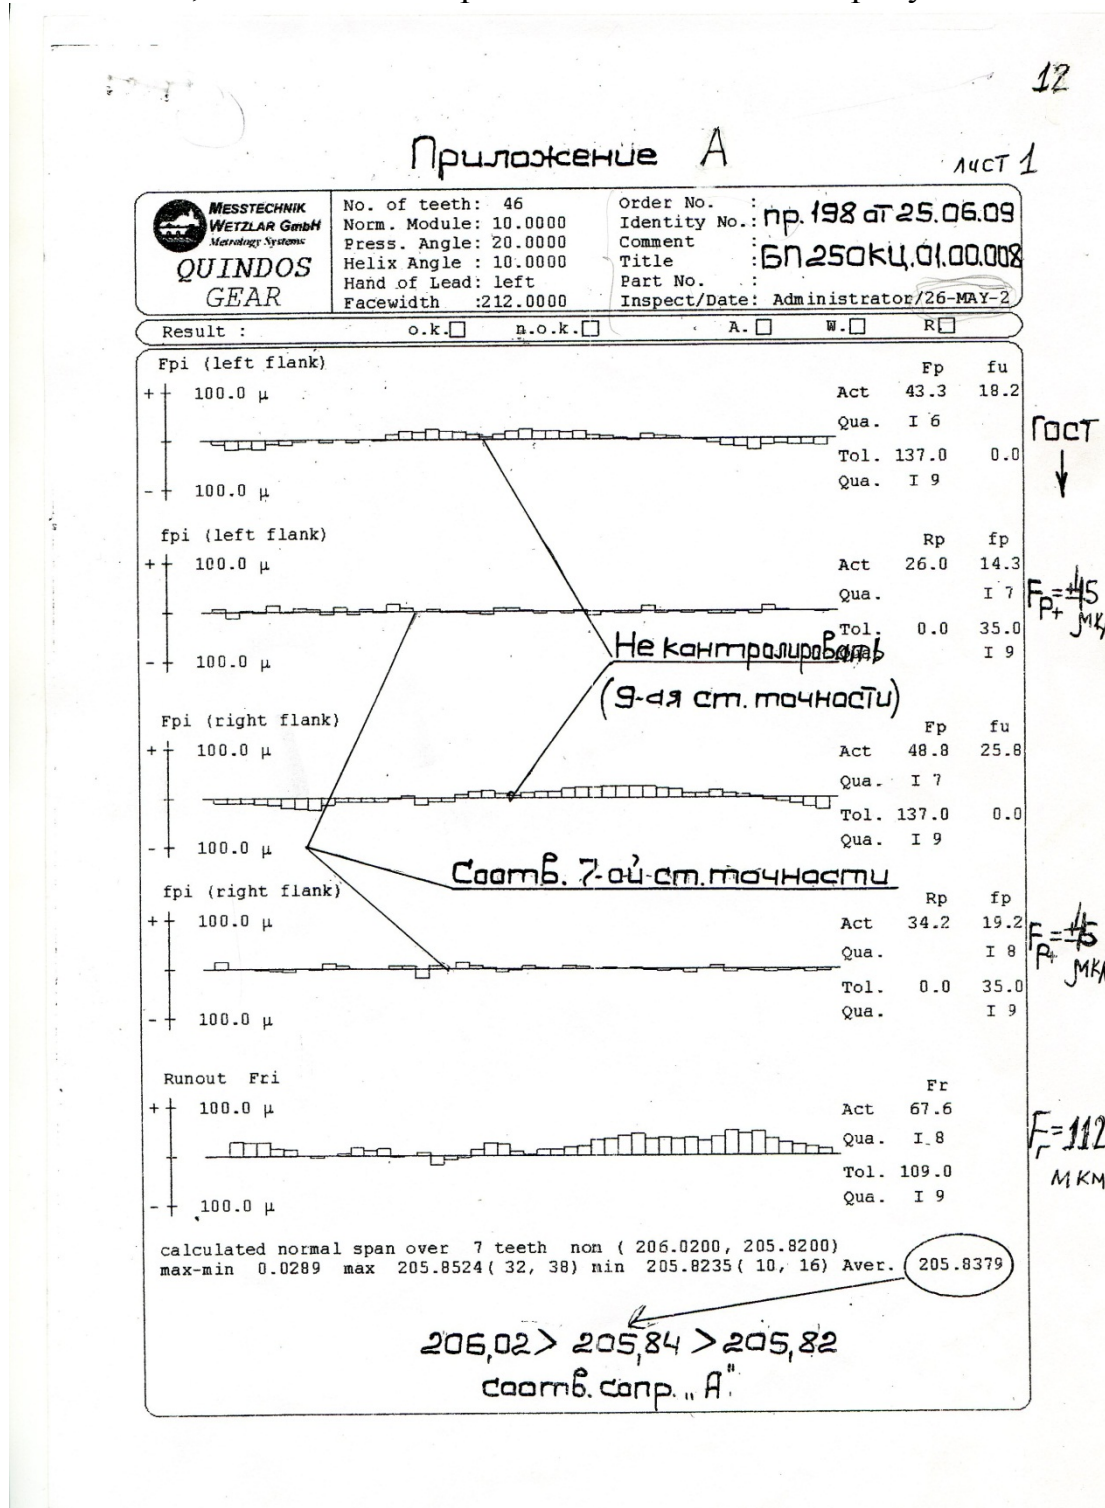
Образец рабочего протокола КИМ для колеса зубчатого цилиндрического БП250КЦ.01.00.008
